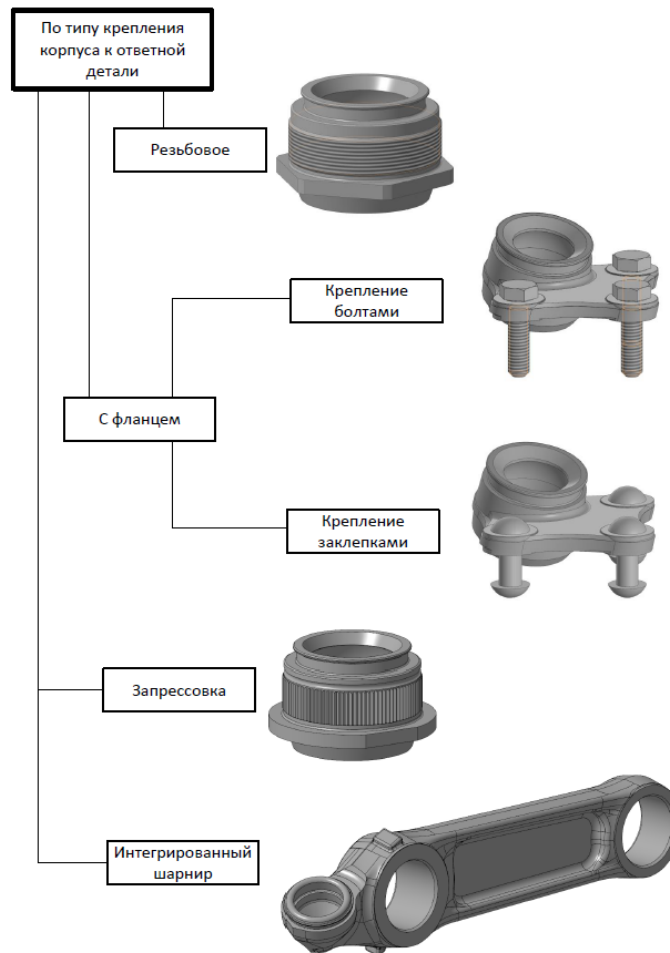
Классификация по типу крепления корпуса к ответной детали
